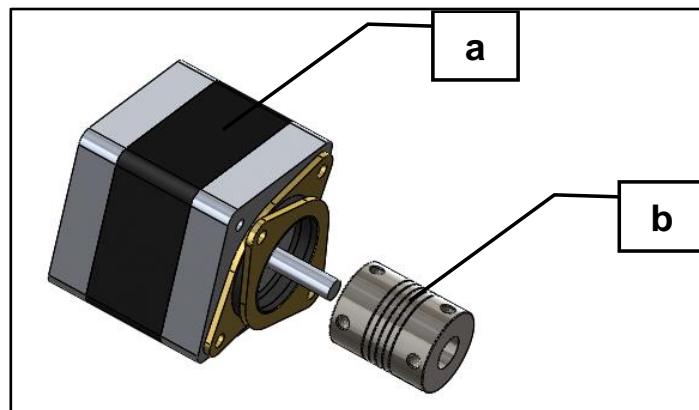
Ensamble del motor nema 17 con el acople flexible para el eje Z
